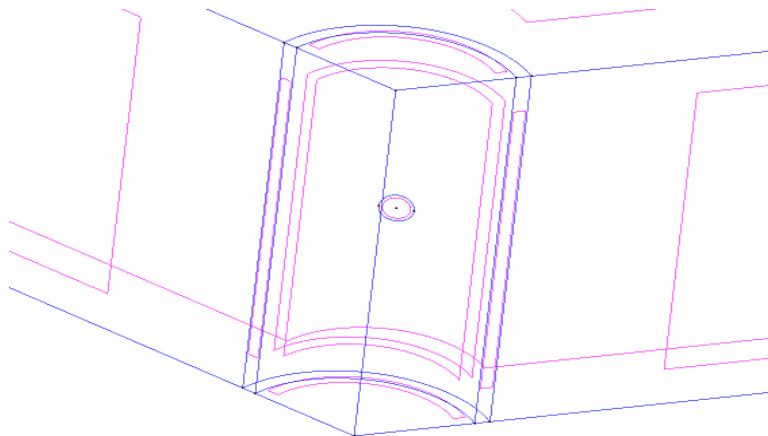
Ubicación de los planos en la sección del casing. [Autor]
